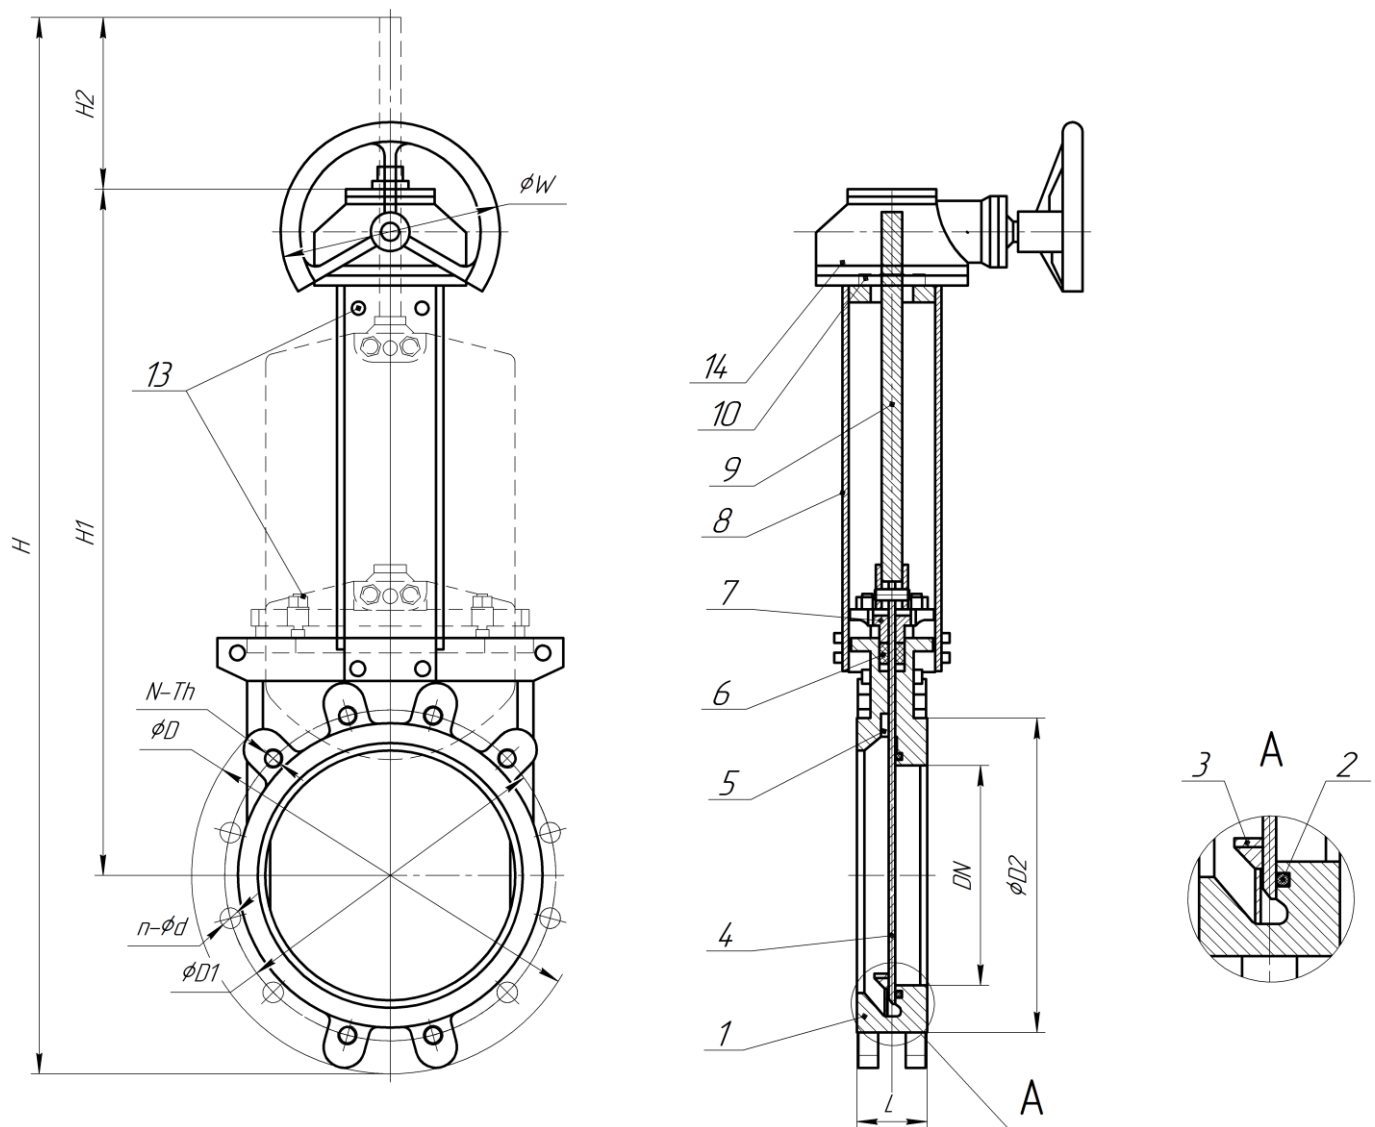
Задвижка с редуктором и выдвижным шпинделем DN50-1000
